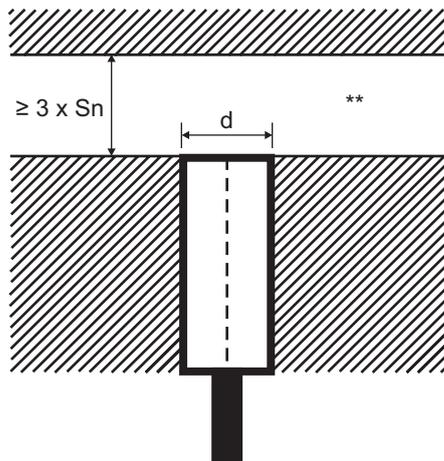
Lange Ausführung, bündiger Einbau, Steckversion
